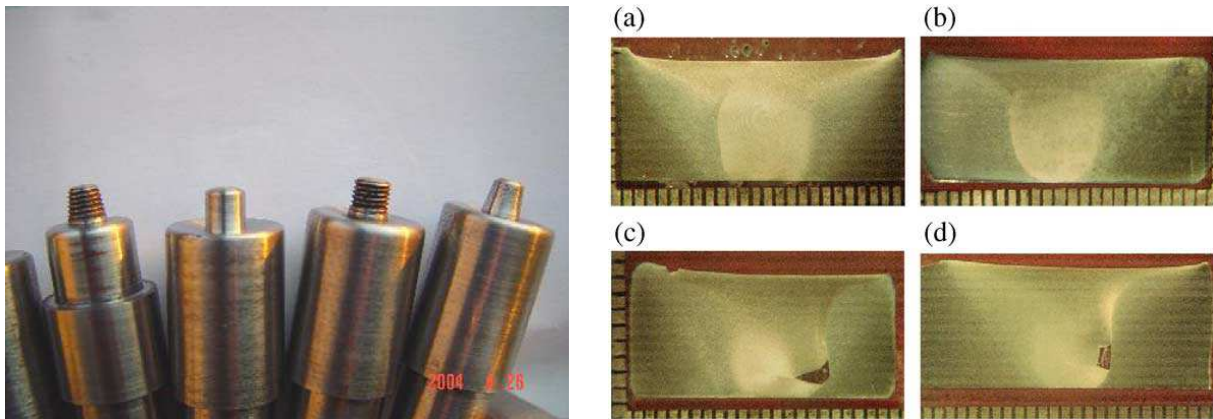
Geometria dos pinos e seções transversais resultantes da soldagem por FSW de uma liga de alumínio 2014. (a) soldagem com ferramenta cilíndrica com rosca, (b) soldagem com ferramenta cônica com rosca, (c) soldagem com ferramenta cilíndrica lisa, (c) soldagem com ferramenta cilíndrica lisa [Zhao et al., 2005].
